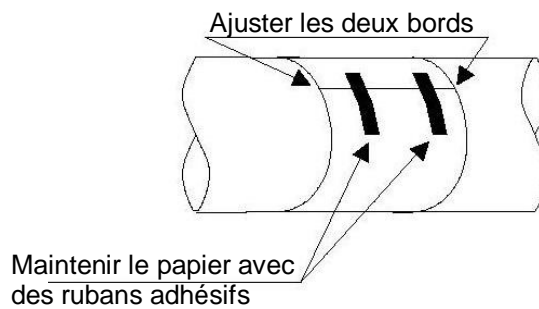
Fixer le papier pour le calibrage
